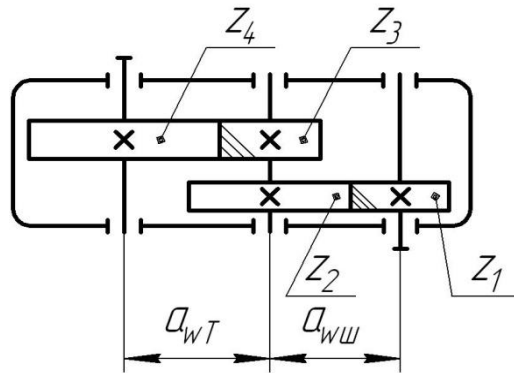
Кінематична схема циліндричного двоступінчастого редуктора типу Ц2У-100-20-21 УЗ
